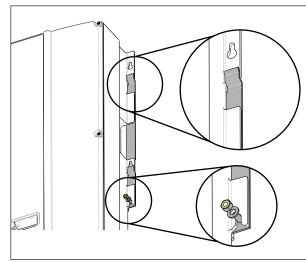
Einhängen des Solar-Wechselrichters in die Montageplatte
